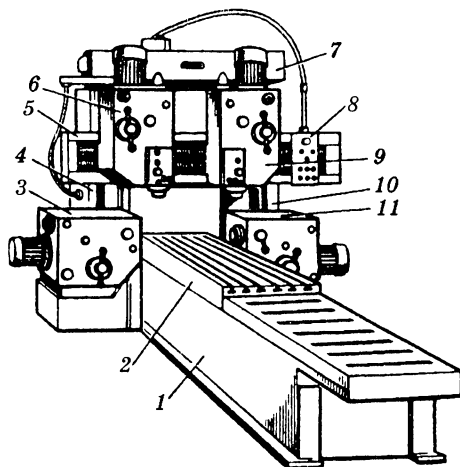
Продольный бесконсольно-фрезерный станок модели 6610:
